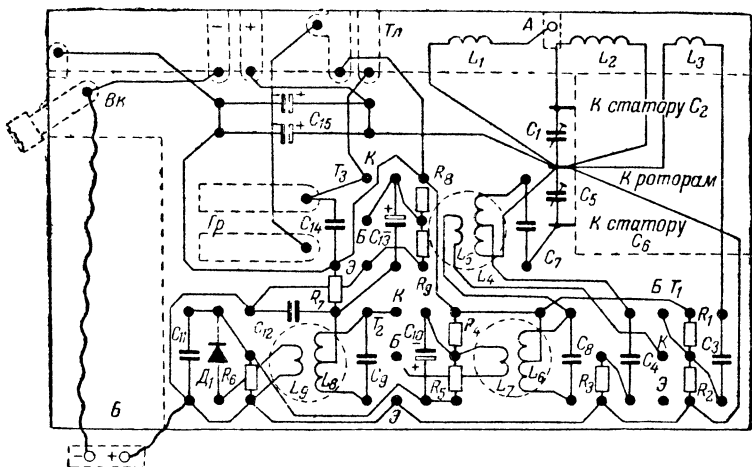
Схема соединений опорных точек деталей на монтажной плате.
